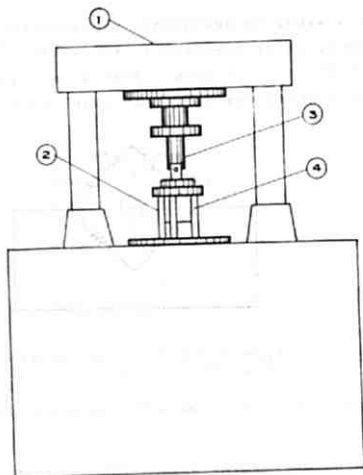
Esquema da montagem do conjunto de equipamentos:
